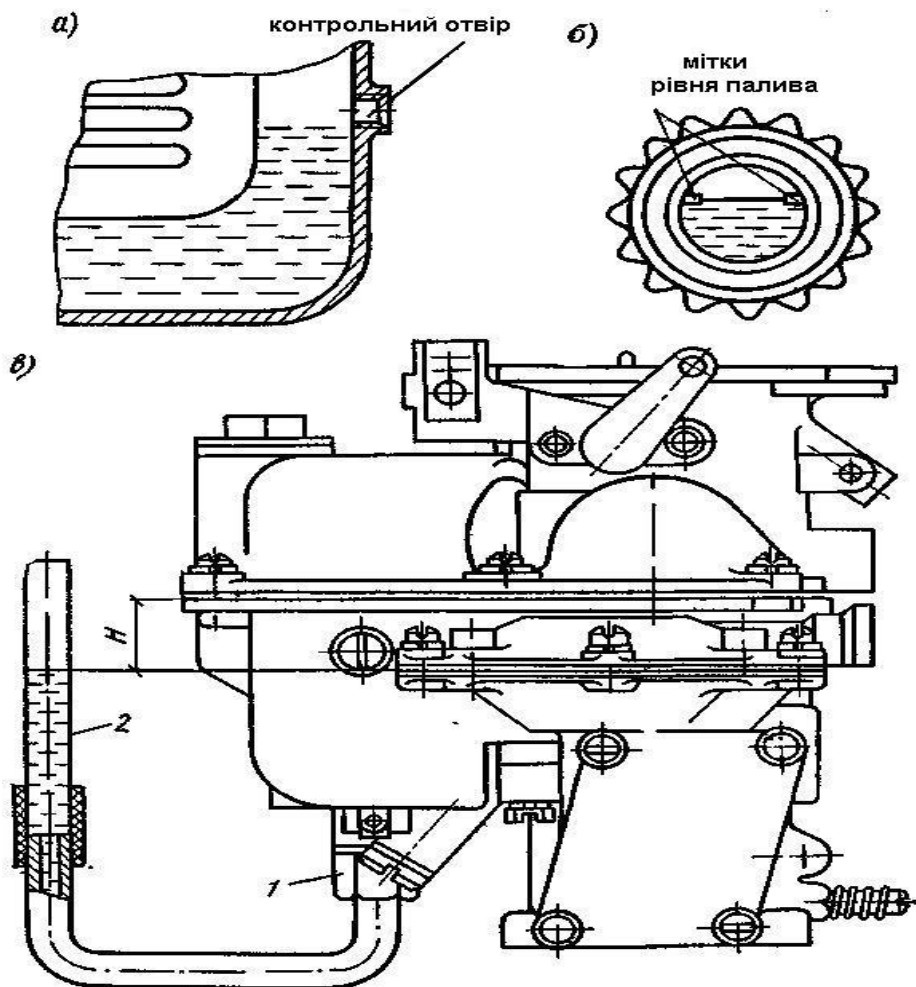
Перевірка рівня палива в поплавковій камері карбюратора
